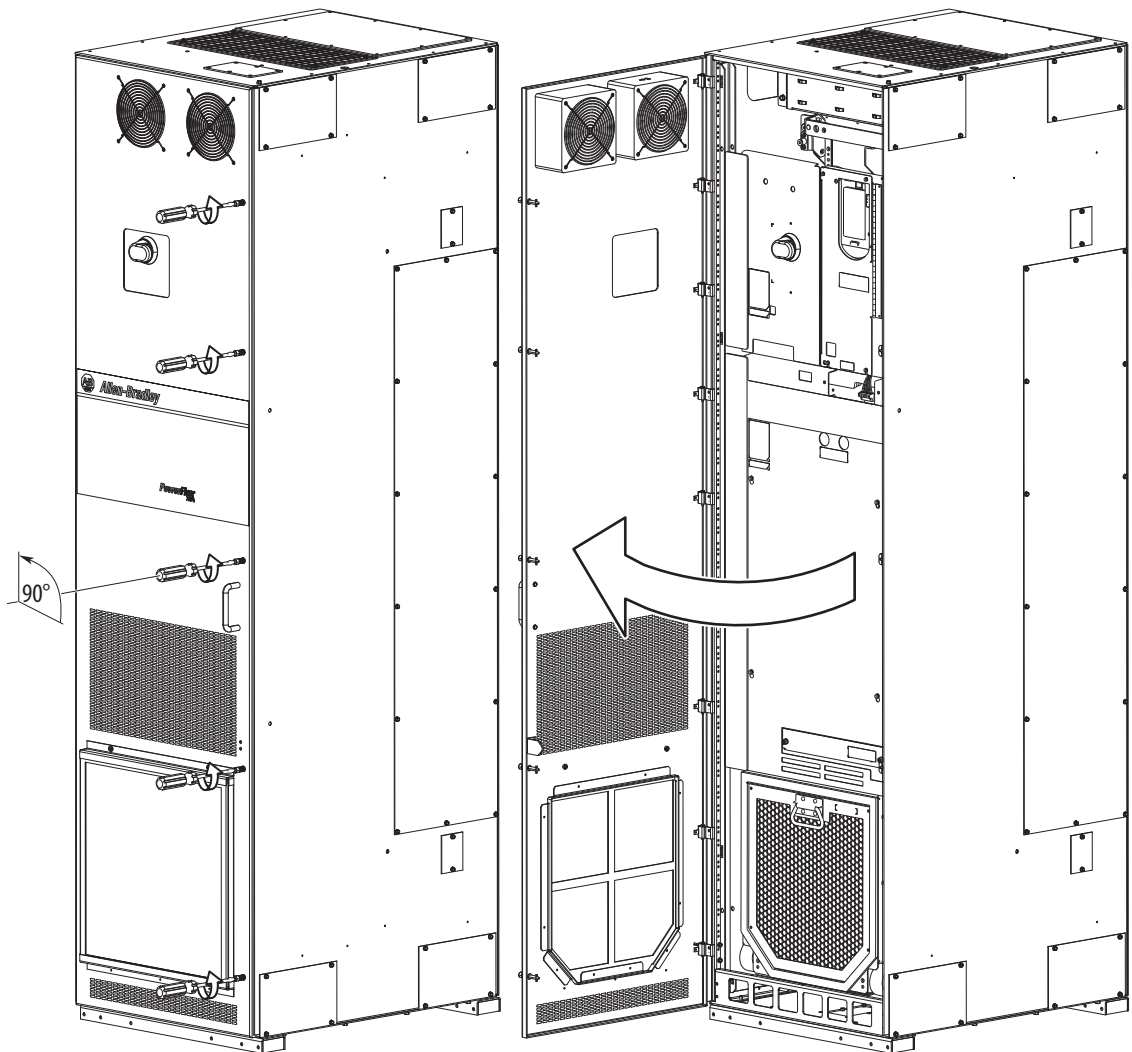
Код корпуса N (IP00, NEMA/UL Open Type), типоразмеры 6 и 7 – дверца
